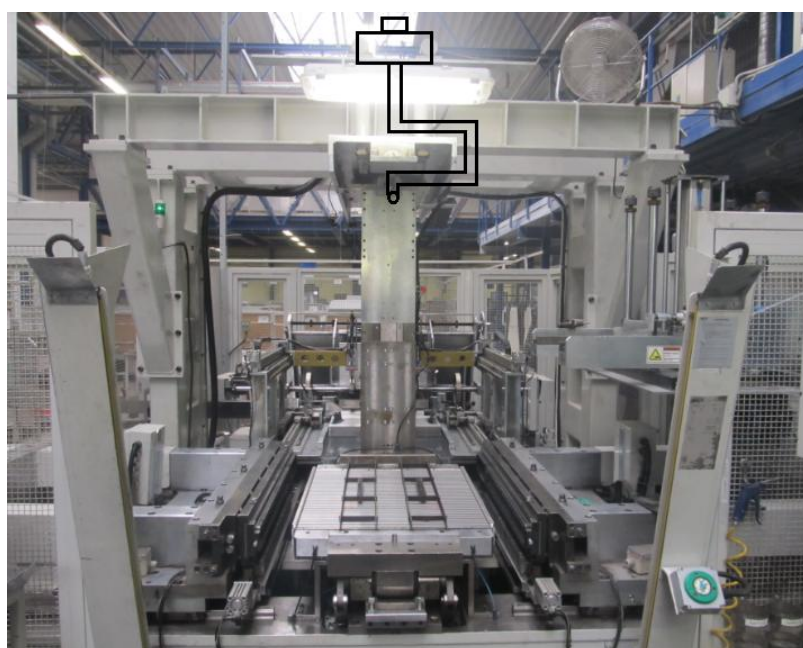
Pneumatický balancér se svedeným ovládáním od balancéru [9]
